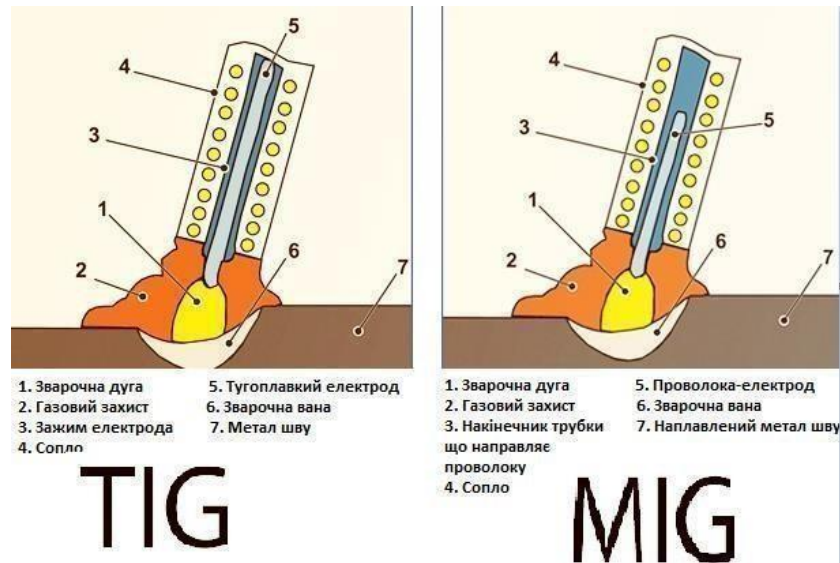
Різниця зварювання методами TIG та MIG
